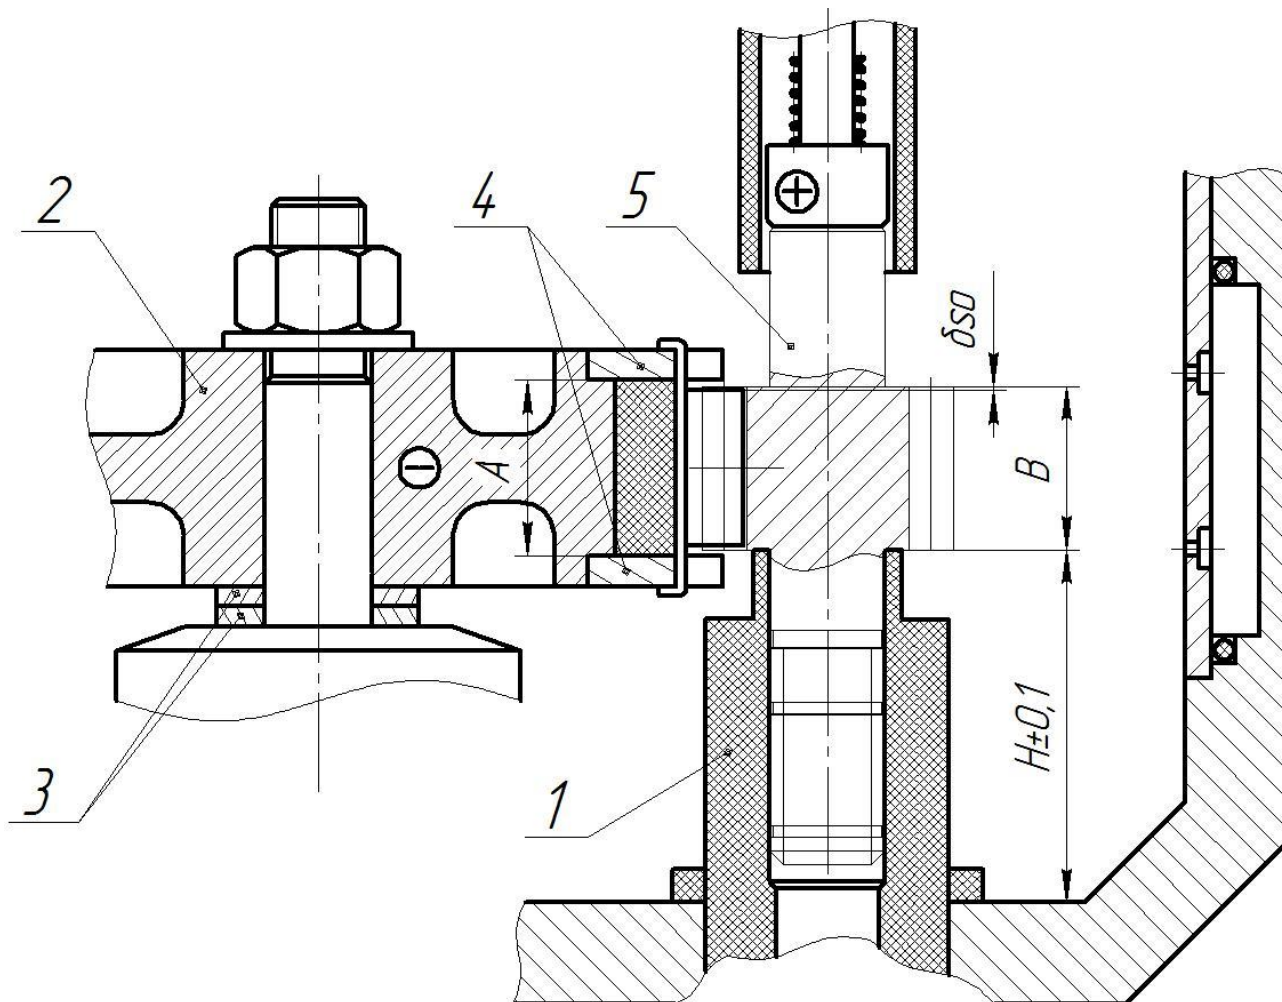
Схема електрохімічної установки для обробки шестерні ведучої
